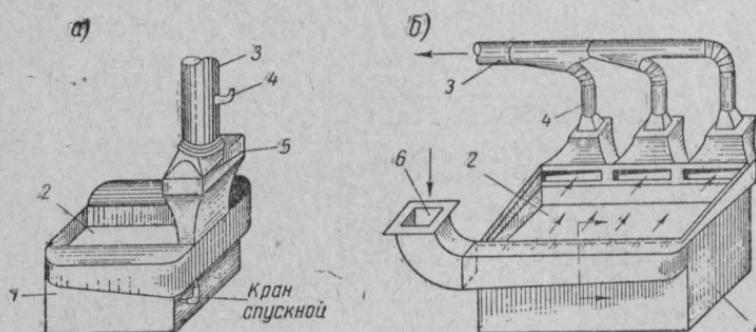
Схема местной вентиляции и горизонтальной воздушной завесы под закалочной ванной:
